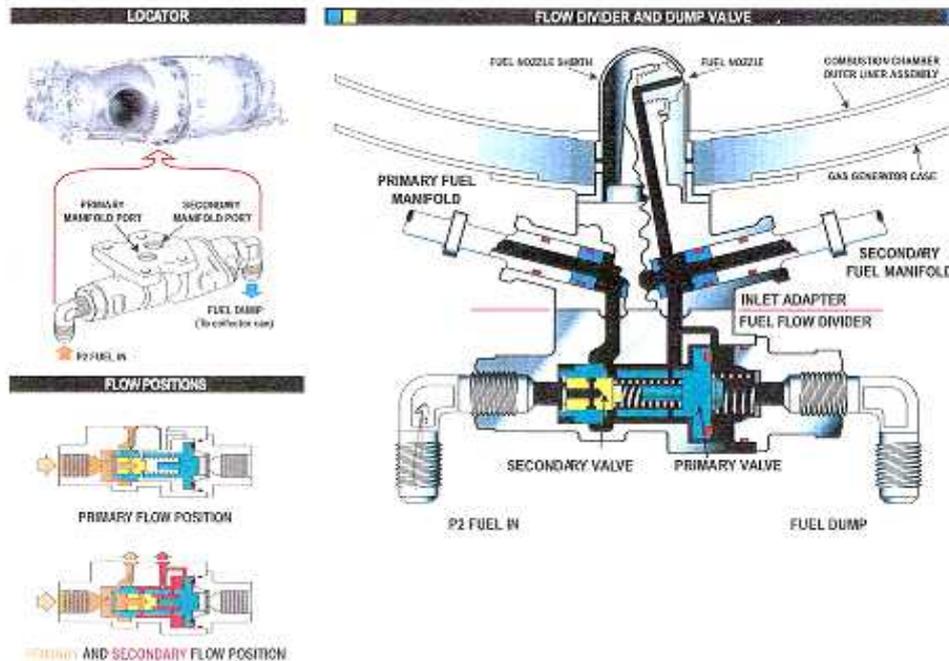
Diviseur d'écoulement de carburant et valve de décharge
